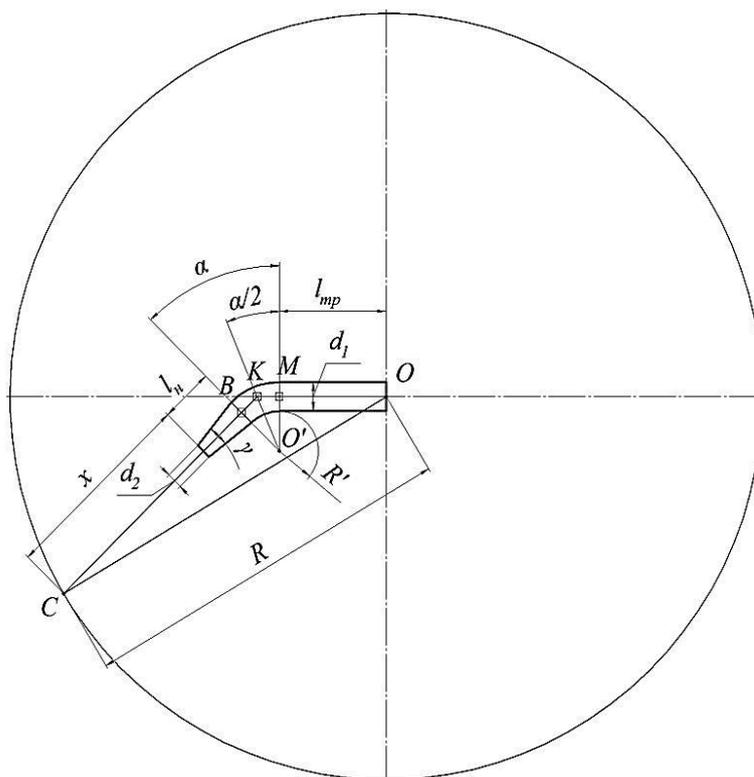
Схема расположения рабочего органа струйного смесителя в цилиндрическом аппарате
